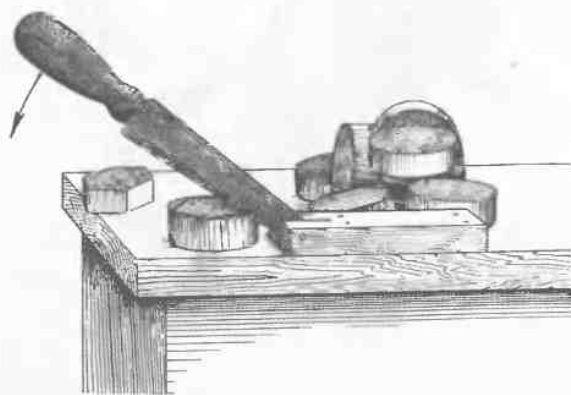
Приспособленный резак из ножа с отверстием для обработки некоторых серийных деталей
